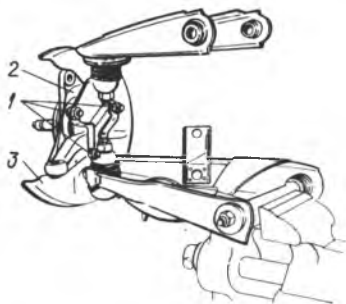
Узел передней подвески левого колеса, закрепленный в тисках для разборки:
